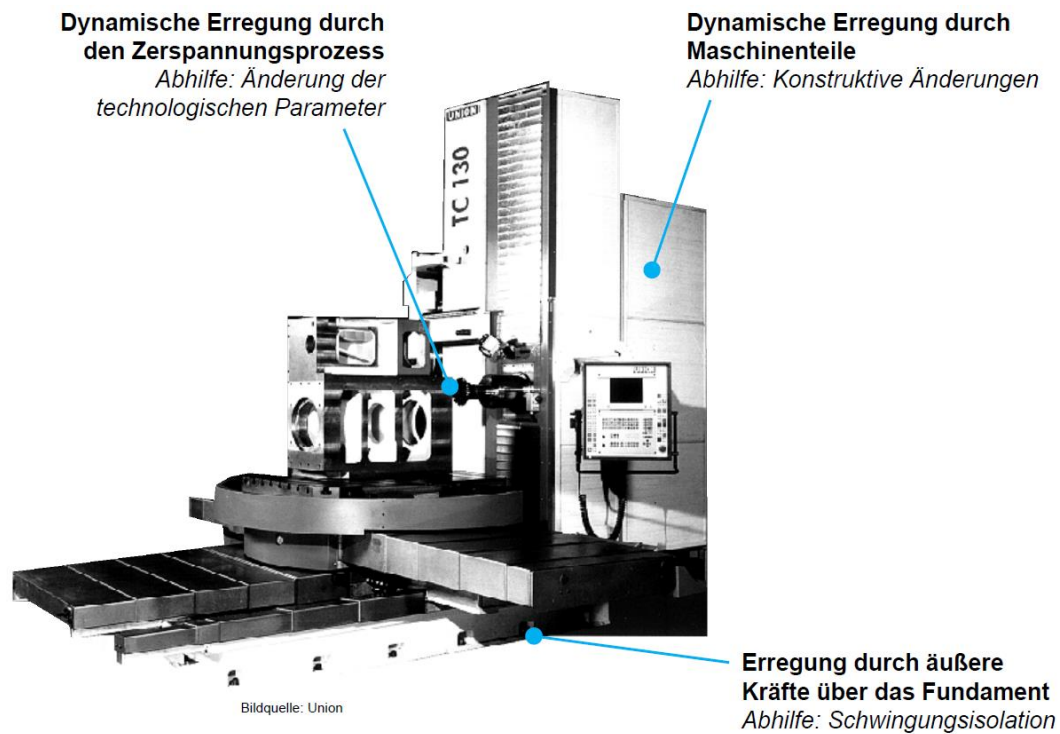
Haupterregungsorte der Schwingungen auf der Werkzeugmaschine [3]
